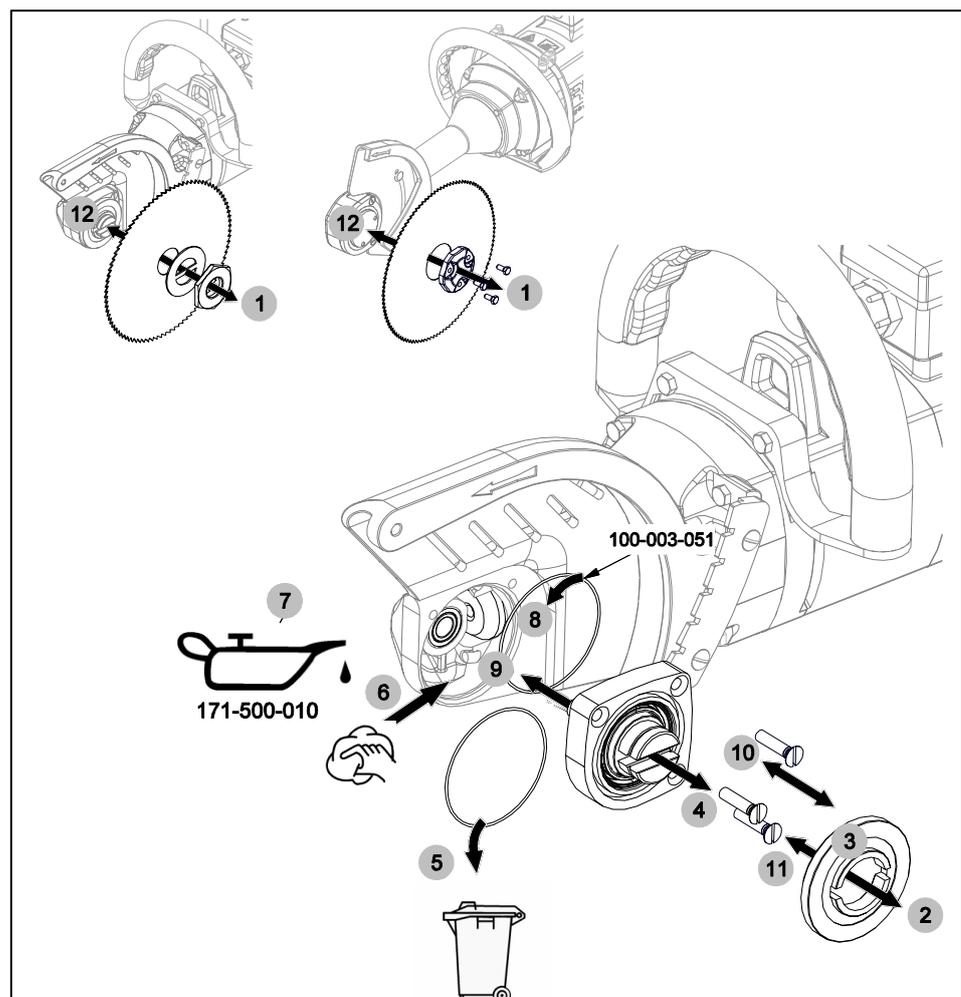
Remplacement de la graisse pour engrenages d'un engrenage à pignons coniques, exemple : K18-01
